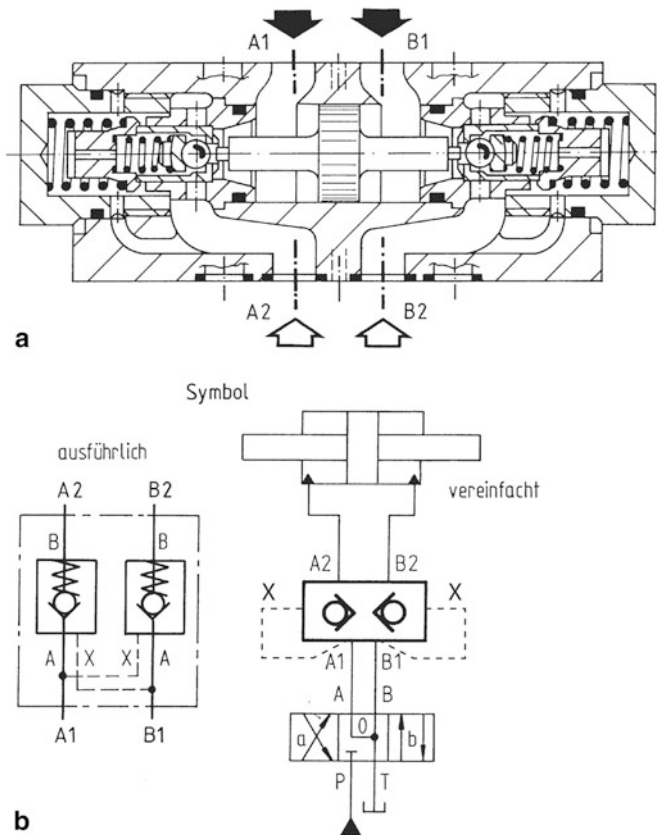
Entsperrbares Zwillings-Rückschlagventil als Aufbauventil mit 2 Flanschanschlüssen (Zwischenplattenventil Sperrblock) (Z 2 S, Bosch Rexroth). a Aufbau mit Öffnung durch interne Druckbeaufschlagung in wechselnder Richtung und Voröffnung, $A1-A2$ freier, $B2-B1$ automatisch entsperrter Durchflussweg oder $B1-B2$ freier, $A2-A1$ automatisch entsperrter Durchflussweg; b Sperrkreisschaltung zur Blockierung des Zylinders in beiden Lastrichtungen
